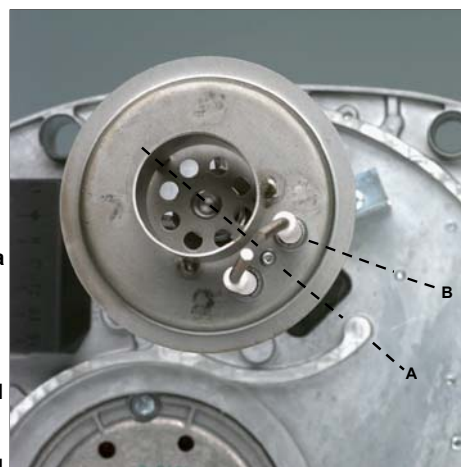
Widok z tyłu: system mieszania RE 1H z zabezpieczeniem przeciw skręcaniu
